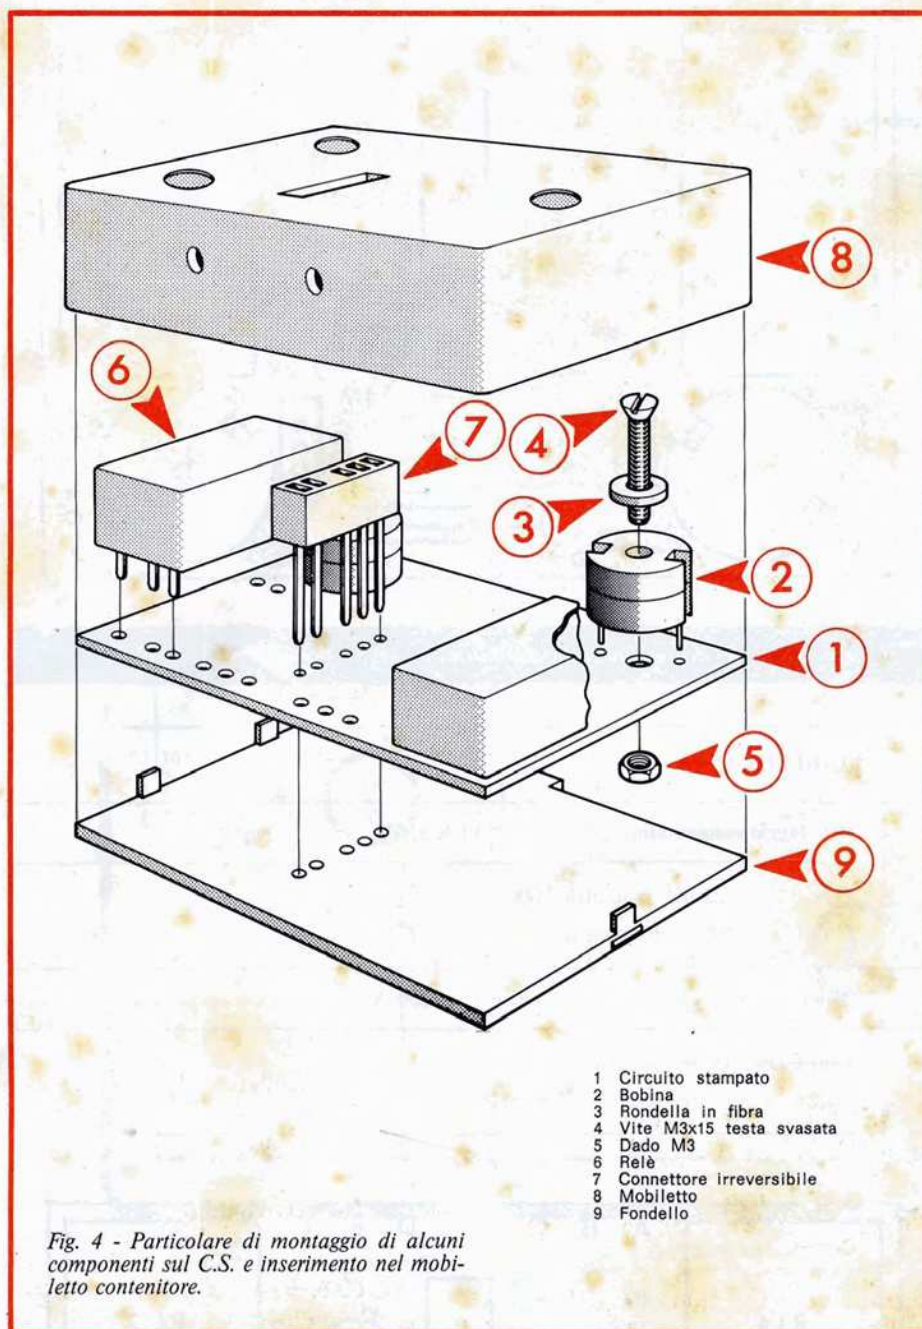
Particolare di montaggio di alcuni componenti sul C.S. e inserimento nel mobilletto contenitore.
